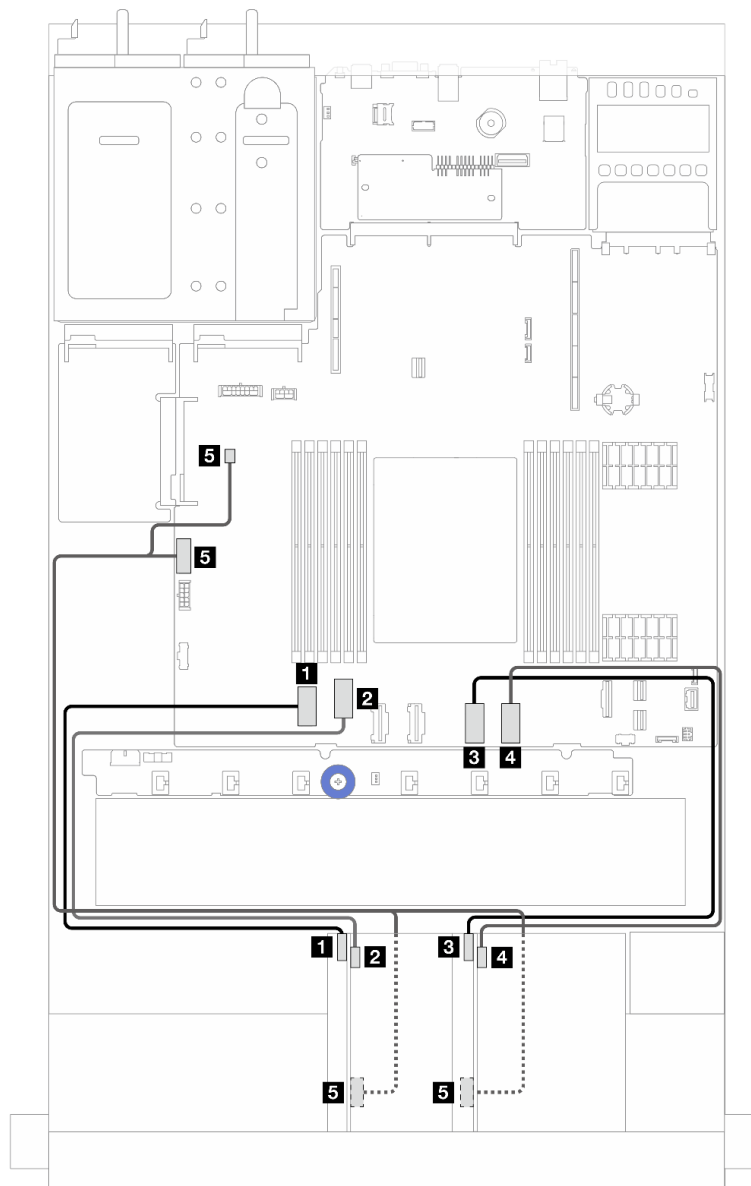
Disposición de los cables para el conjunto de expansión frontal
